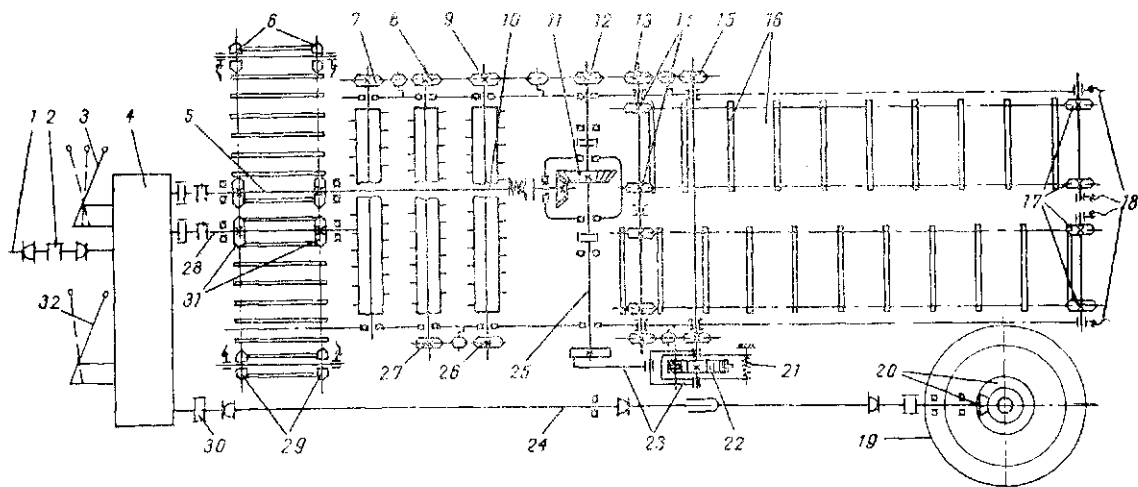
Кинематическая схема кормораздатчика РЗМ-8,0П1:
